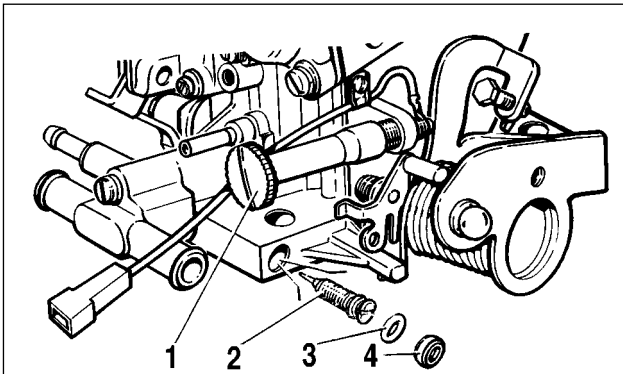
Stellschrauben für Leerlaufeinrichtung:
